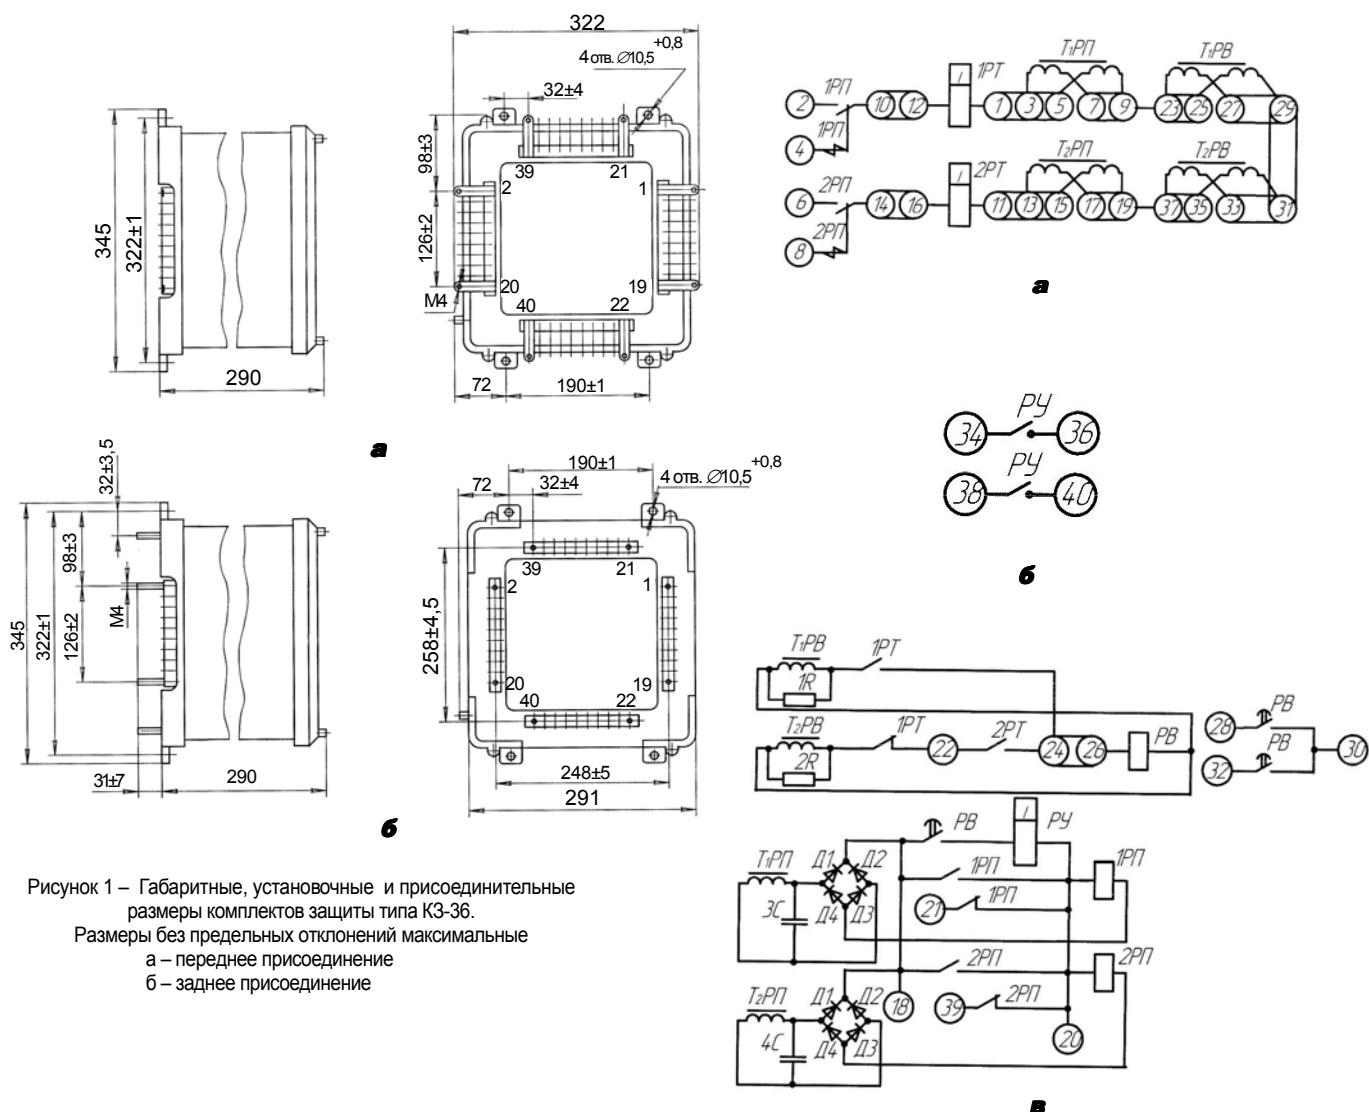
Габаритные, установочные и присоединительные размеры комплектов защиты типа КЗ-36.
